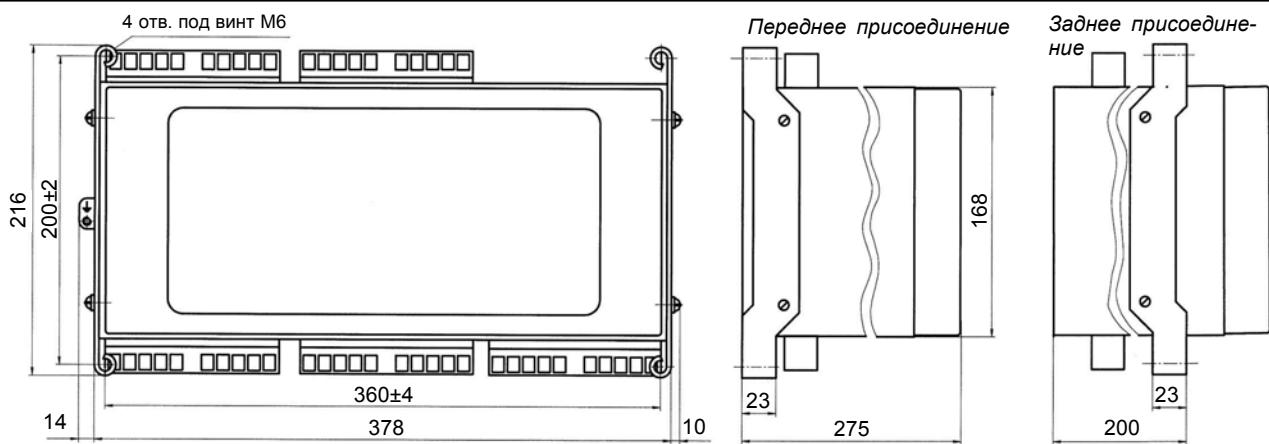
Габаритные, установочные размеры блока типа БЭ 2604
